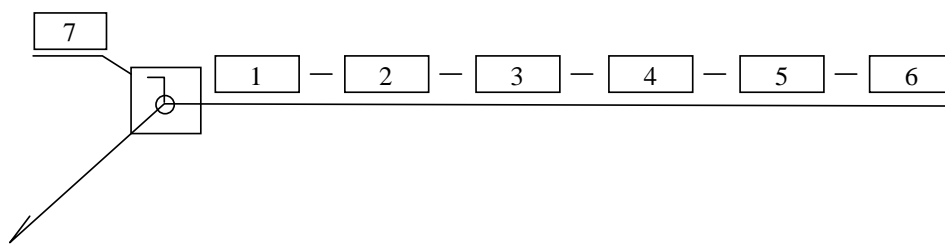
Обозначение сварных швов на чертежах по ГОСТ 2.312-72:
